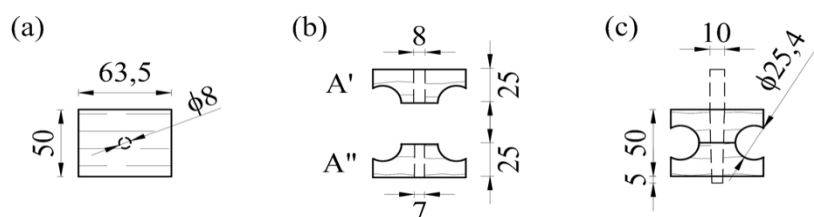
Dimensões dos corpos de prova (mm) (a) vista superior; (b) vista frontal; (c) vista frontal após a
